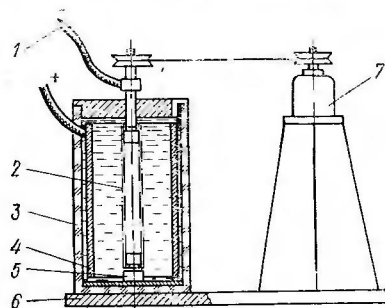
Установка для равномерного меднения наружной поверхности цилиндрических деталей:
